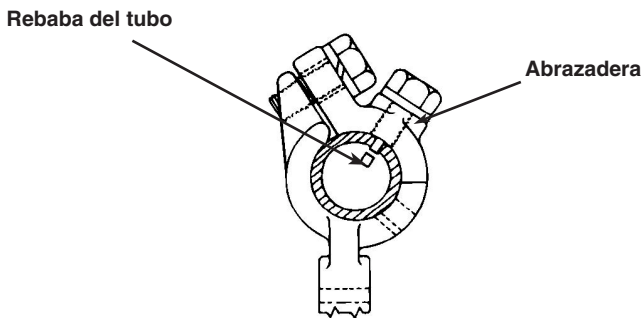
Tubo de operación Instalado con el Tornillo sujetador de la abrazadera, completamente ajustado y el Tornillo de retención perforante en posición final, una vez que el tubo ha sido perforado.
